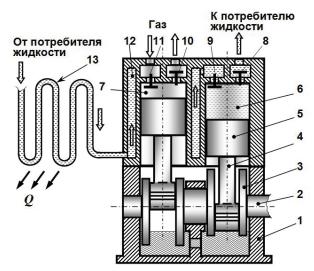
Конструктивная схема поршневой ГМОД с двумя цилиндрами и тронковыми поршнями:
